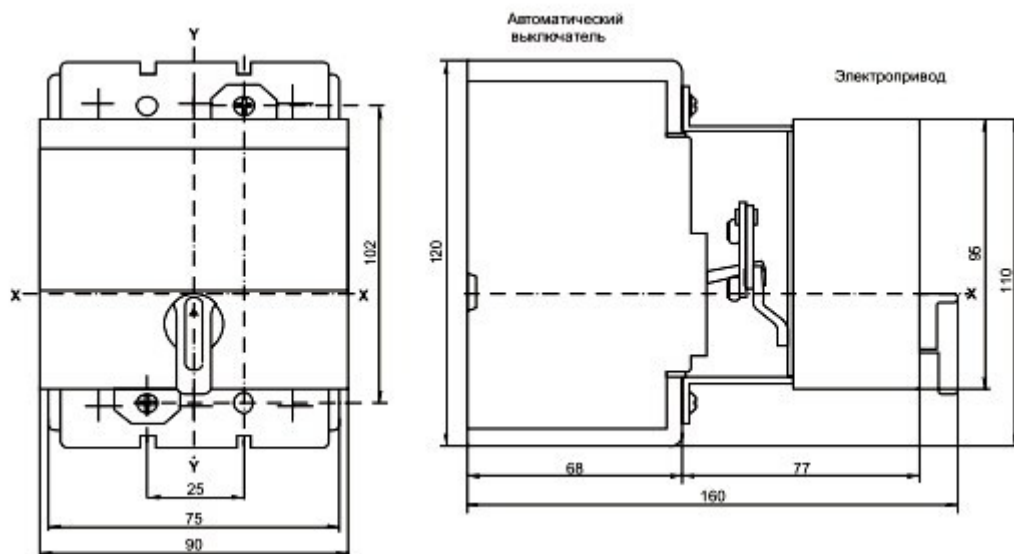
Габаритные размеры выключателя ВА88-32 с электроприводом ЭП-32/33
